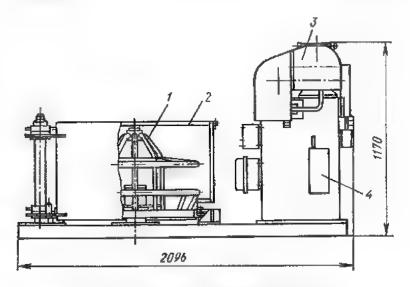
Станок для перемотки проволоки: 1— буктодержатель, 2— защитвый кожук, 3— наматыватель, 4— правідьное
